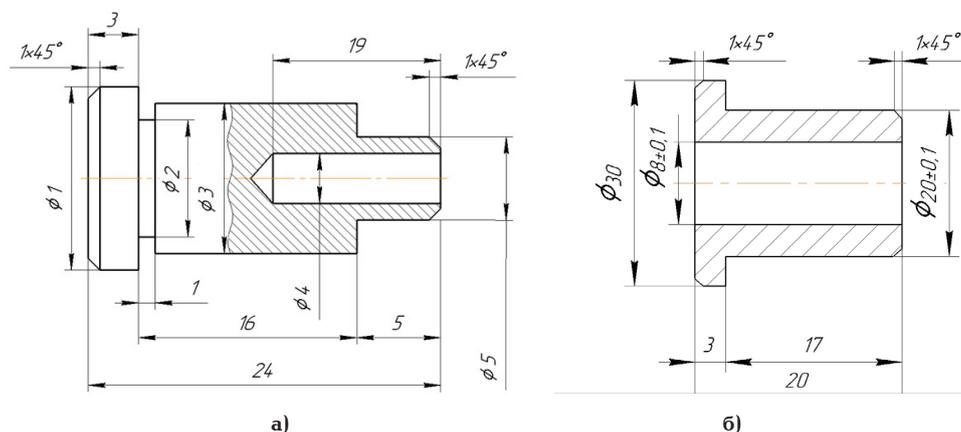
Условный чертёж штока для измерения хода иглы с диаметром игл распылителей от 8,0 до 18 мм (а). Втулка крепежная разрезная (б)
